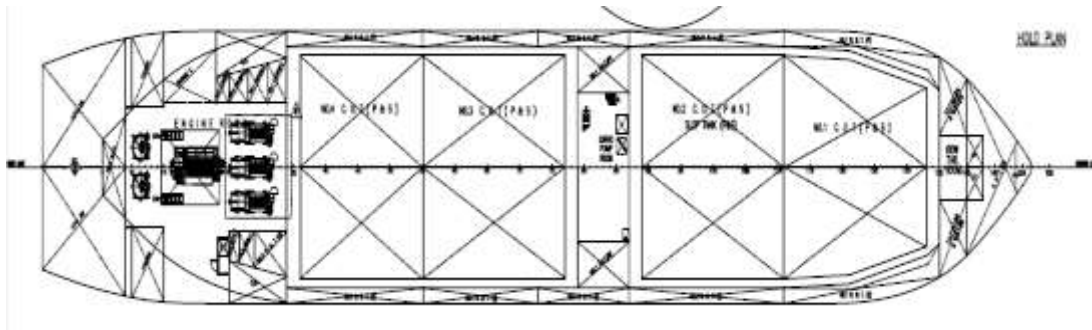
Disposición de tanques. Fuente: Planos de capacidad del buque.
